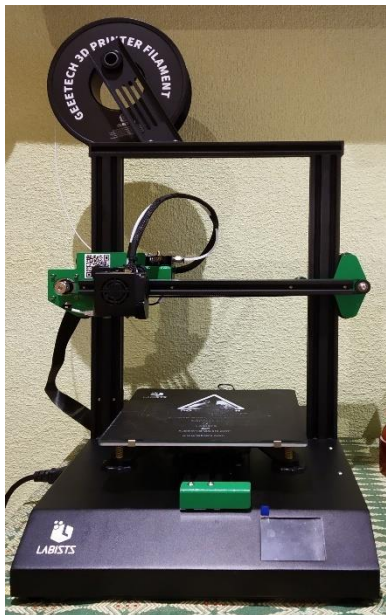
Impresora 3D utilizada para crear el molde. Autor: Elaboración propia.
